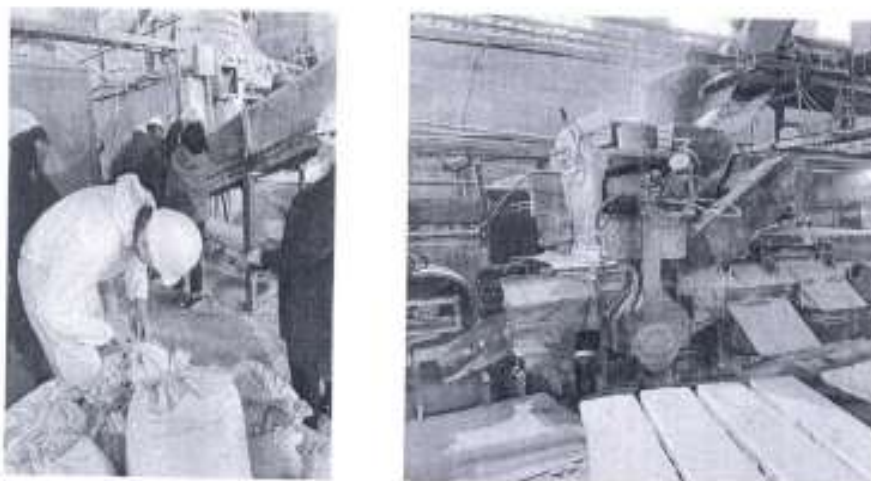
Процесс подготовки сырья для подачи в бункер полусухого прессования.
